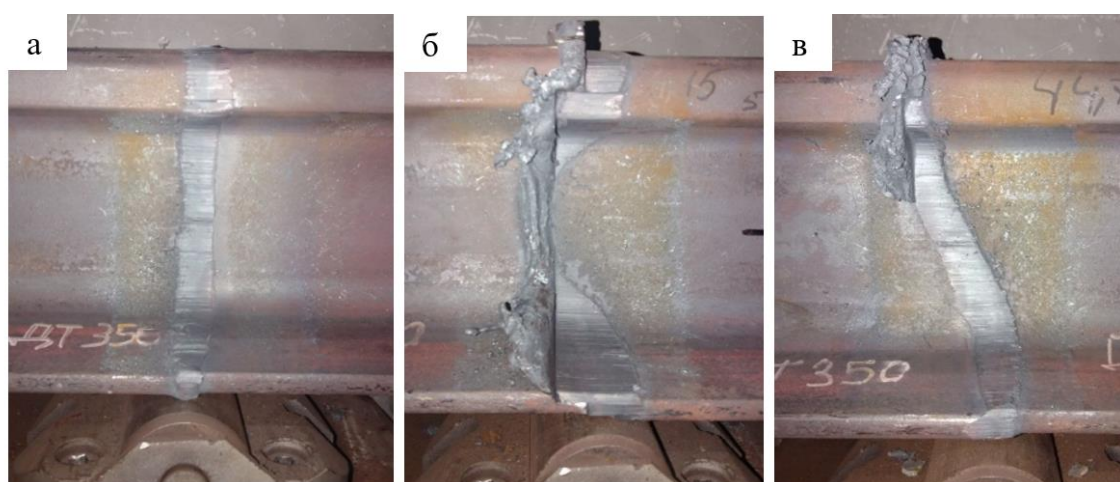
Позиционирование пуансона на сварных пробах перед испытаниями:
